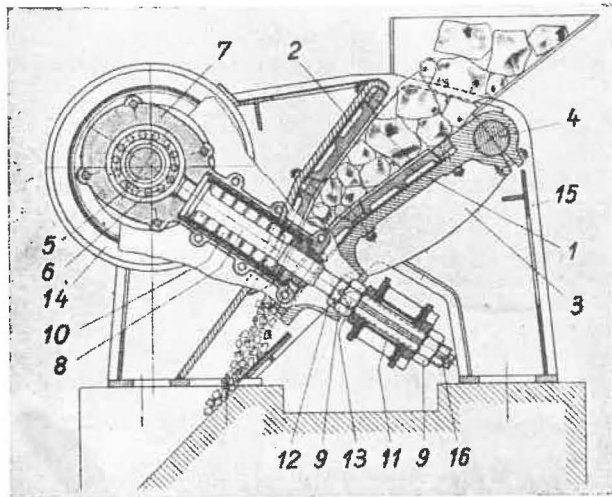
Concasseur à mâchoire Stahlbau Rheinhausen.
